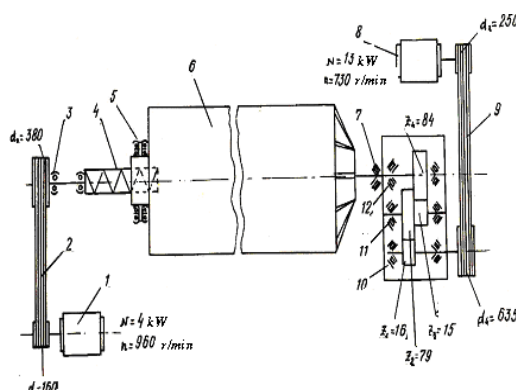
Кинематическая схема хлопковой сушилки марки 2СБ-10.
